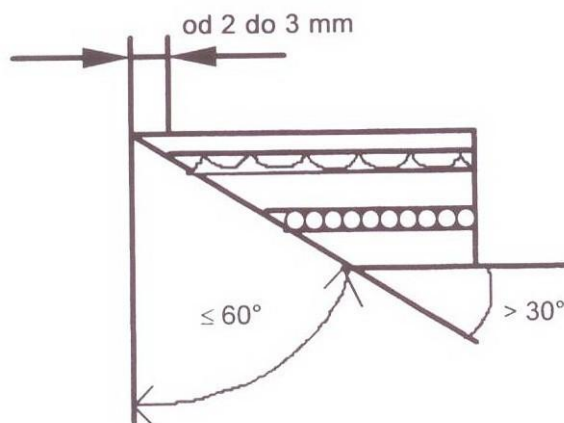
Opracovanie skiel VSG – hladko brúsená hrana
